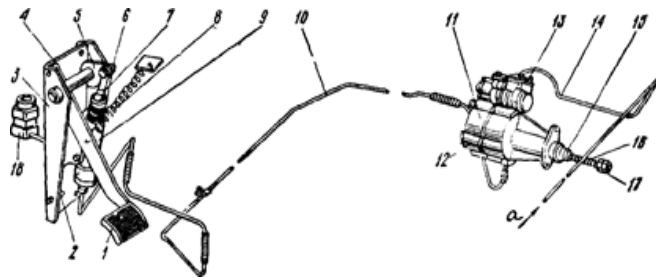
Привод механизма сцепления: 1-педаля; 2- упор нижний; 3- кронштейн; 4- упор верхний; 5- рычаг; 6-палец эксцентриковый; 7- толкатель поршня; 8- пружина оттяжная; 9- цилиндр главный; 10-трубопровод гидравлический; 11-усилитель пневмогидравлический; 12-пробка; 13-клапан перепускной; 14-трубопровод пневматический; 15-чехол защитный; 16- толкатель поршня; 17-гайка сферическая регулировочная; 18-бачок компенсационный; а- сжатый воздух
